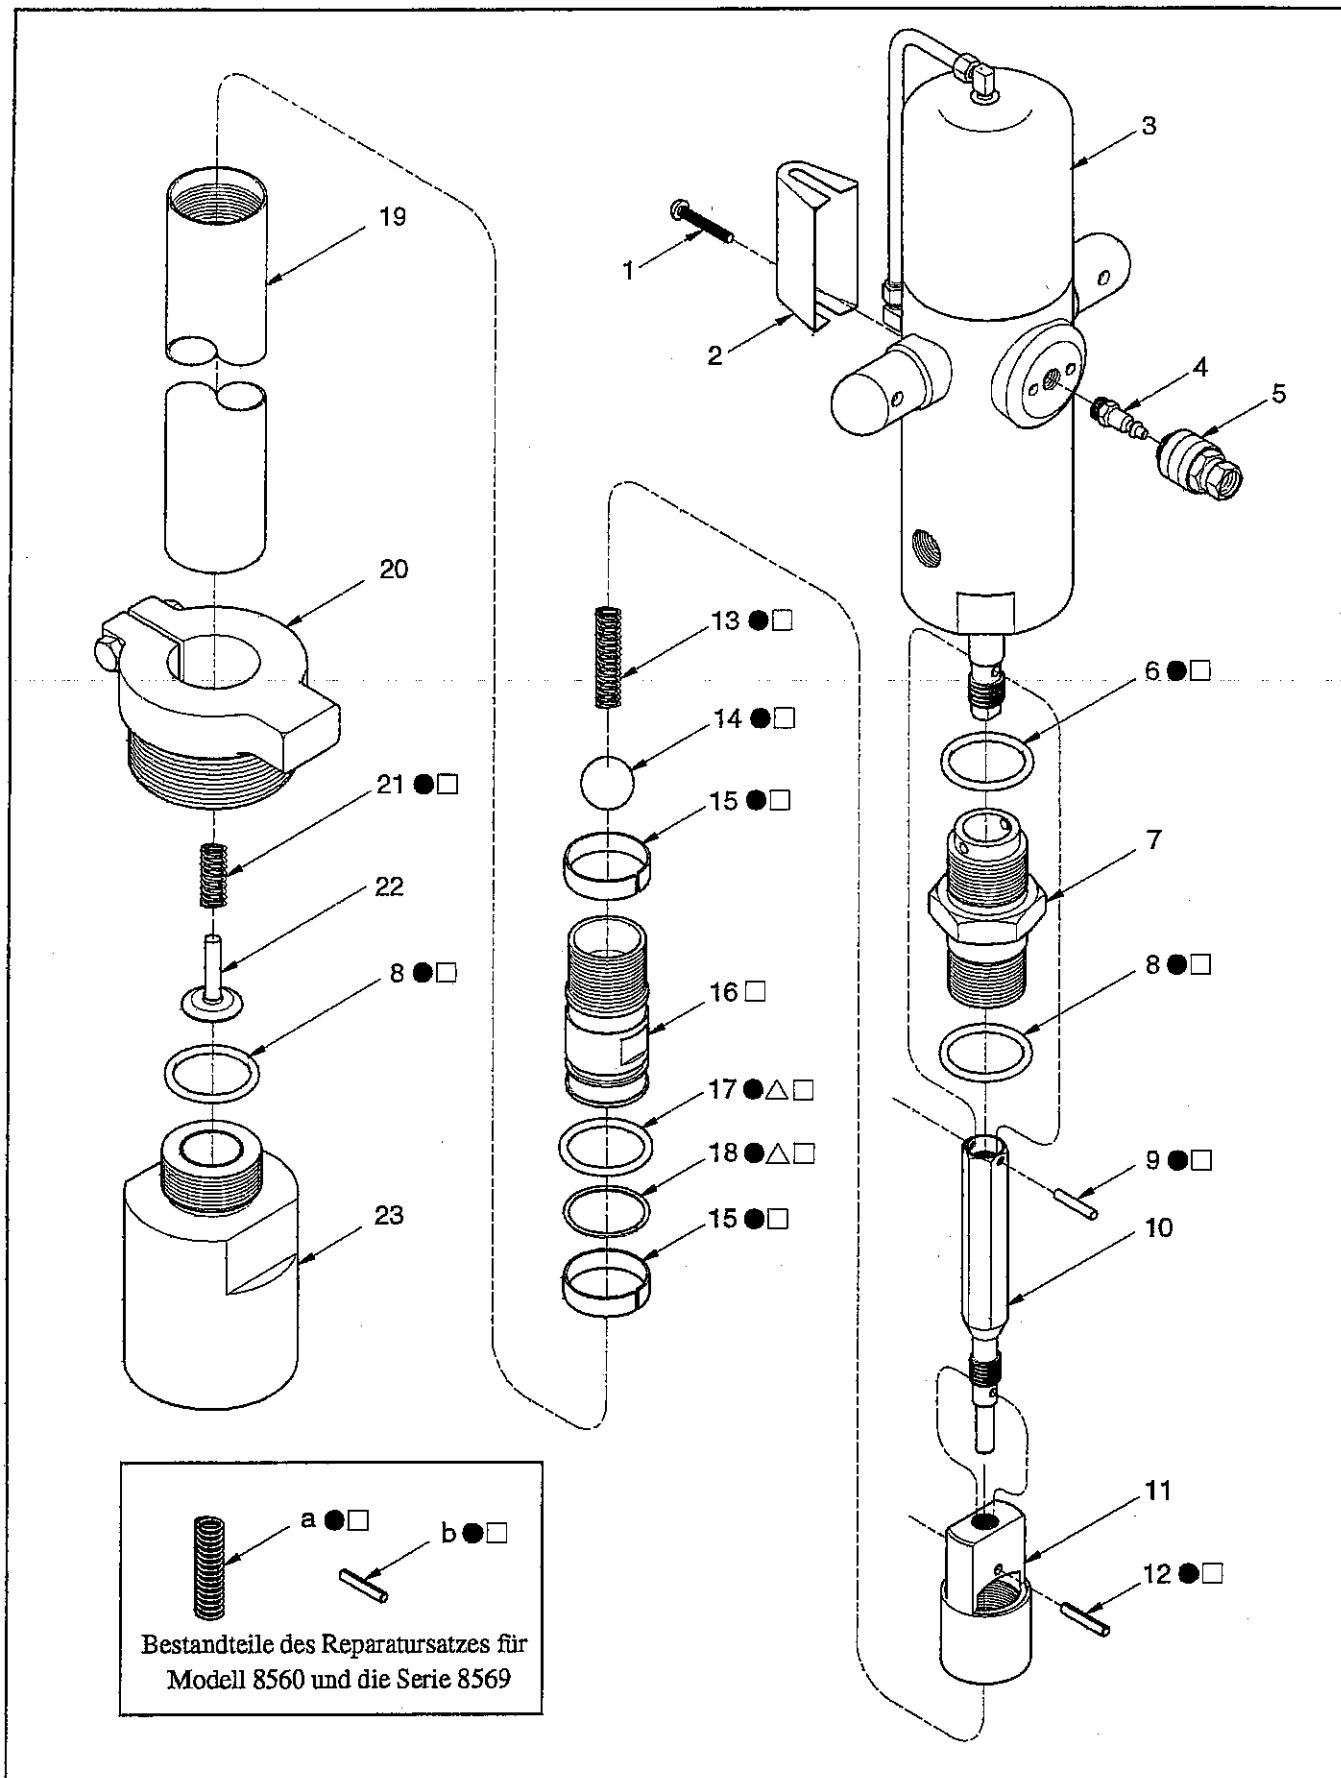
Mit mittlerem Druck betriebene Stutzenpumpe, Modell 8568 - Explosionszeichnung
